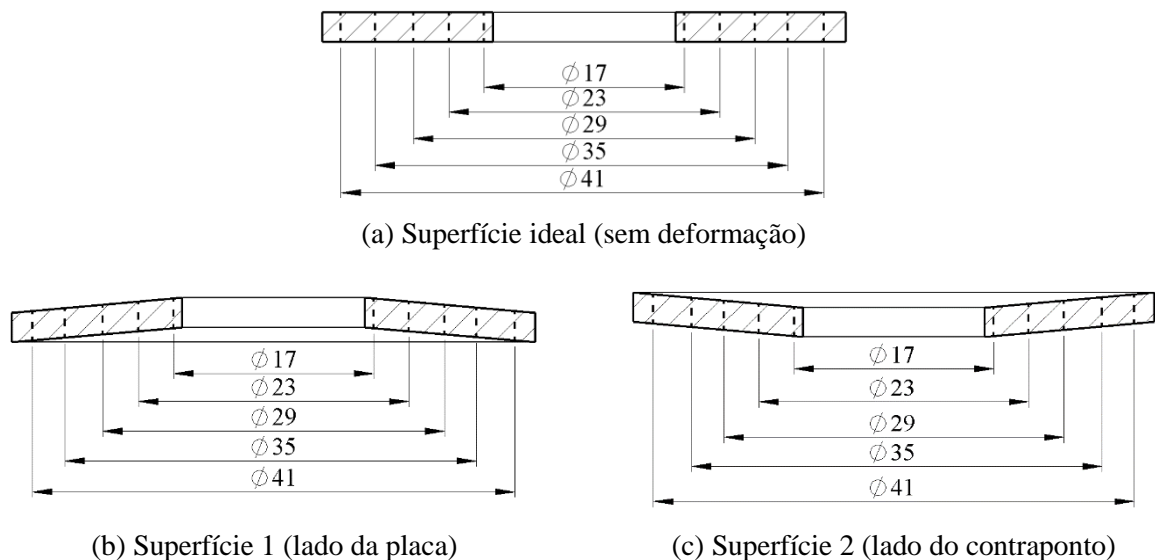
Representação gráfica da deformação das superfícies usinadas: (a) Superfície ideal; (b) Superfície 1; (c) Superfície 2 (dimensões em mm).
